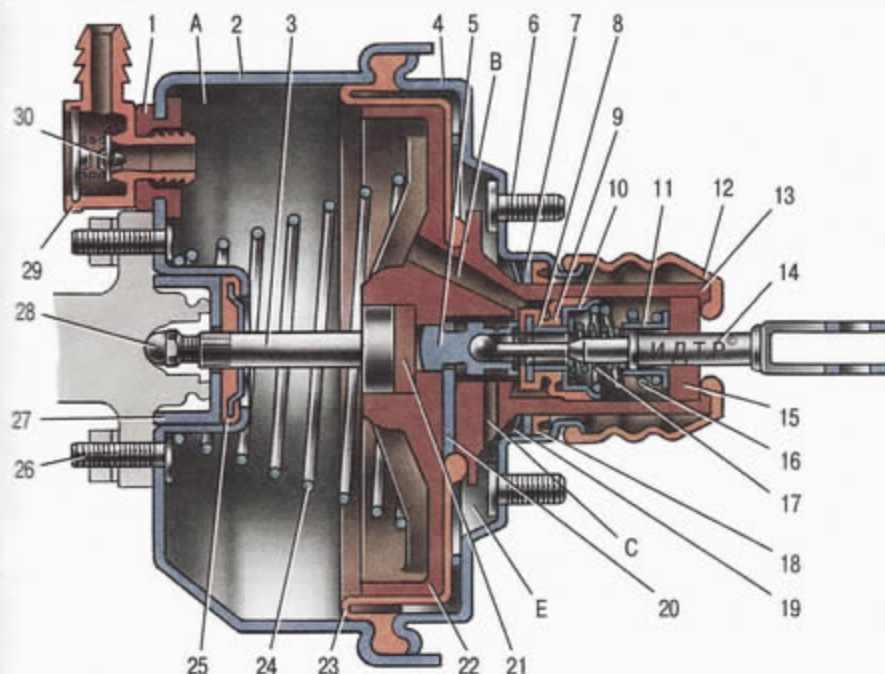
Вакуумный усилитель тормозов: 1 – уплотнитель наконечника шланга; 2 – корпус усилителя; 3 – шток; 4 – крышка; 5 – поршень; 6 – болт крепления усилителя; 7 – дистанционное кольцо; 8 – опорная чашка пружины клапана; 9 – клапан; 10 – опорная чашка клапана; 11 – опорная чашка возвратной пружины; 12 – защитный колпачок; 13 – обойма защитного колпачка; 14 – толкатель; 15 – возвратный фильтр; 16 – возвратная пружина клапана; 17 – пружина клапана; 18 – уплотнитель крышки корпуса; 19 – стопорное кольцо; 20 – упорная пластина; 21 – буфер; 22 – корпус клапана; 23 – диафрагма; 24 – возвратная пружина корпуса клапана; 25 – уплотнитель штока; 26 – болт крепления главного цилиндра; 27 – обойма уплотнителя штока; 28 – регулировочный болт; 29 – наконечник шланга; 30 – обратный клапан; А – вакуумная полость; В – канал, соединяющий вакуумную полость с внутренней полостью клапана; С – канал, соединяющий внутреннюю полость клапана с атмосферной полостью; Е – атмосферная полость
